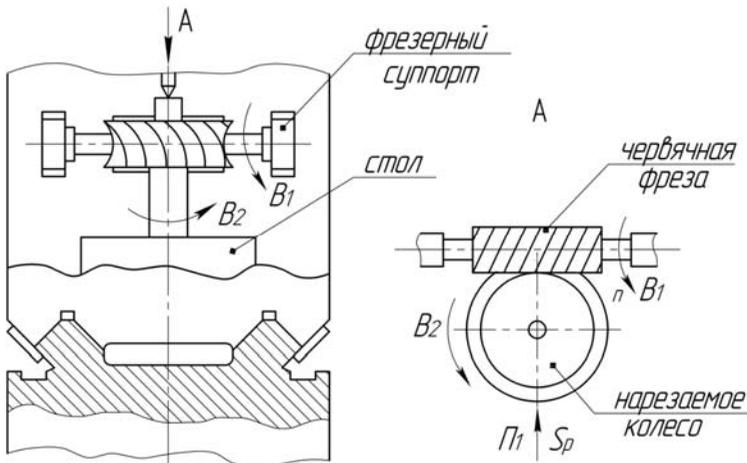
Рабочая зона зубофрезерного станка и формообразующие движения при нарезании червячного колеса с радиальной подачей стола
